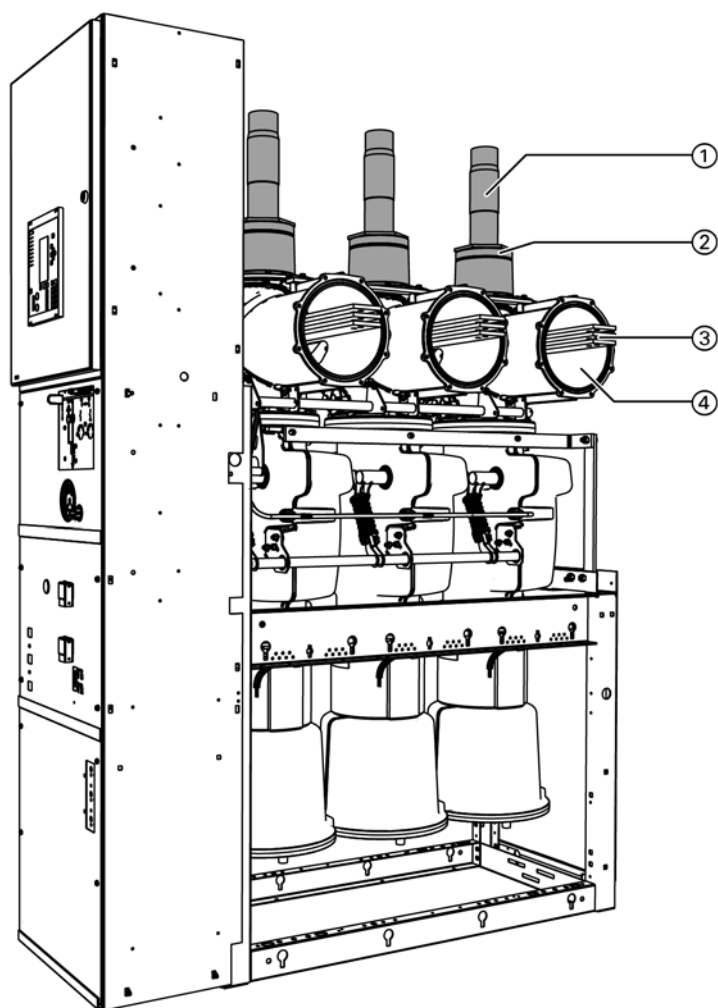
Обзор компоновки сборных шин: шина с изоляцией из твердого диэлектрика без трехпозиционного разъединителя
